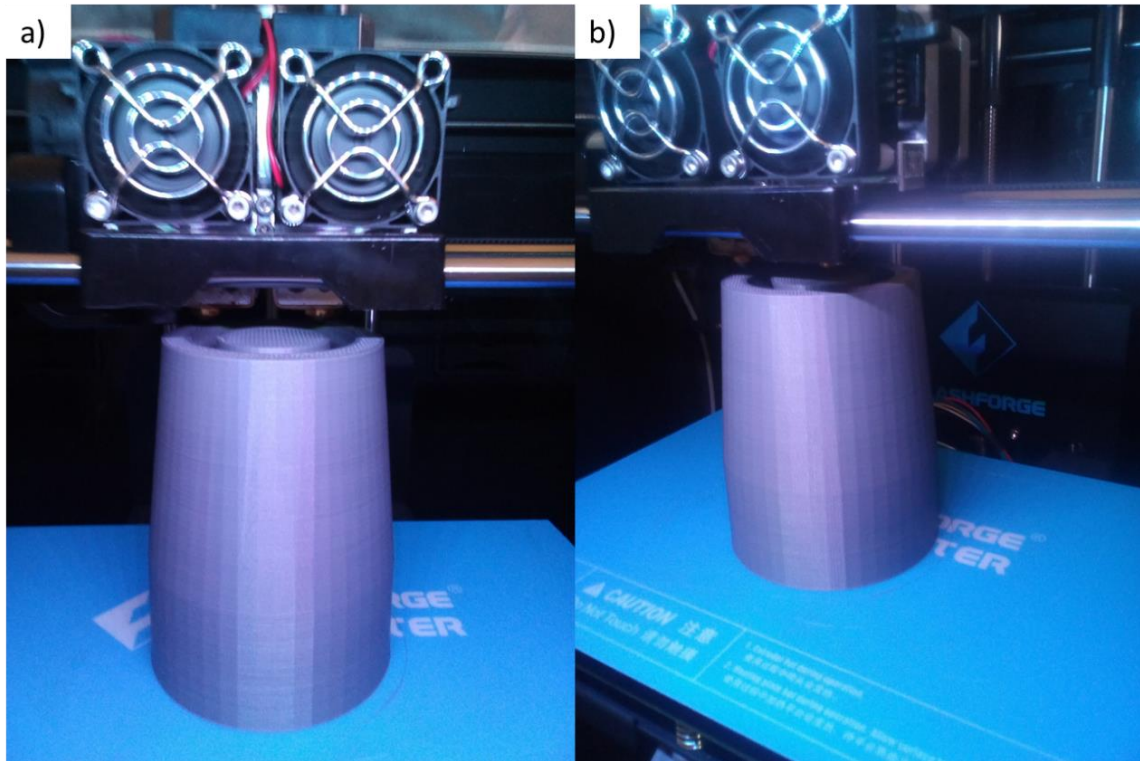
Manufactura de boquillas mediante impresión tridimensional
